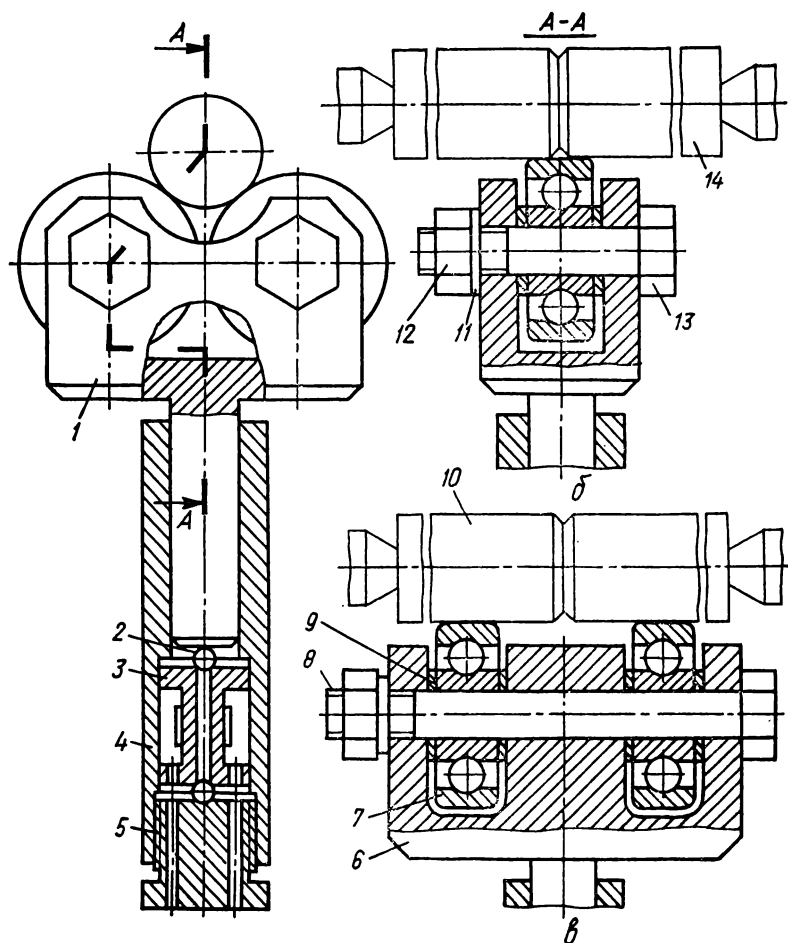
Общий вид приспособления (а) со сменными вилками для трехточечного (б) и четырехточечного (в) нагружений образца поперечной нагрузкой при создании кольцевой трещины:
